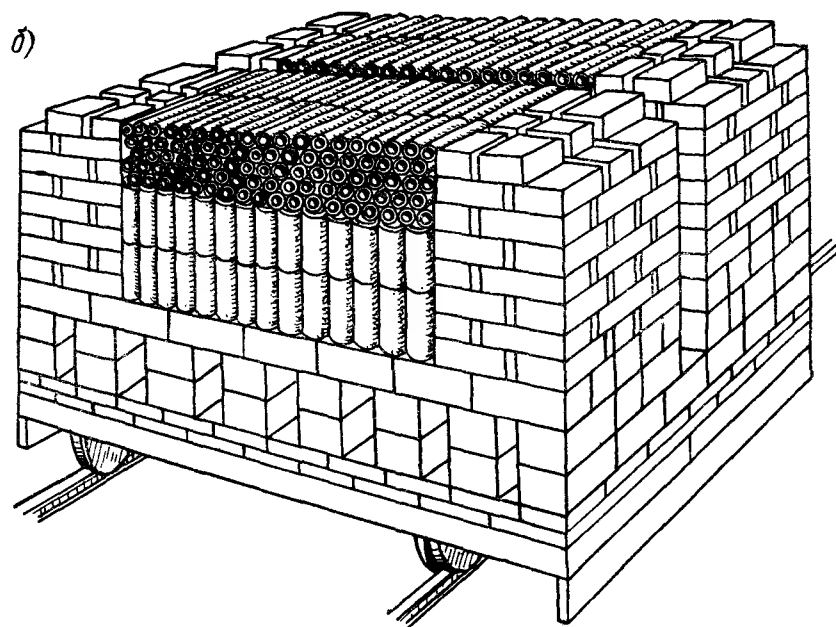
Комбинированная садка дренажных труб на вагонетку туннельной печи
